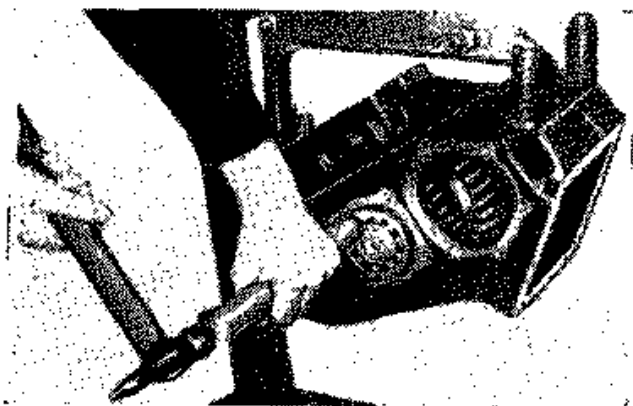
Запрессовка заднего подшипника в сборе с промежуточным валом в отверстие картера
